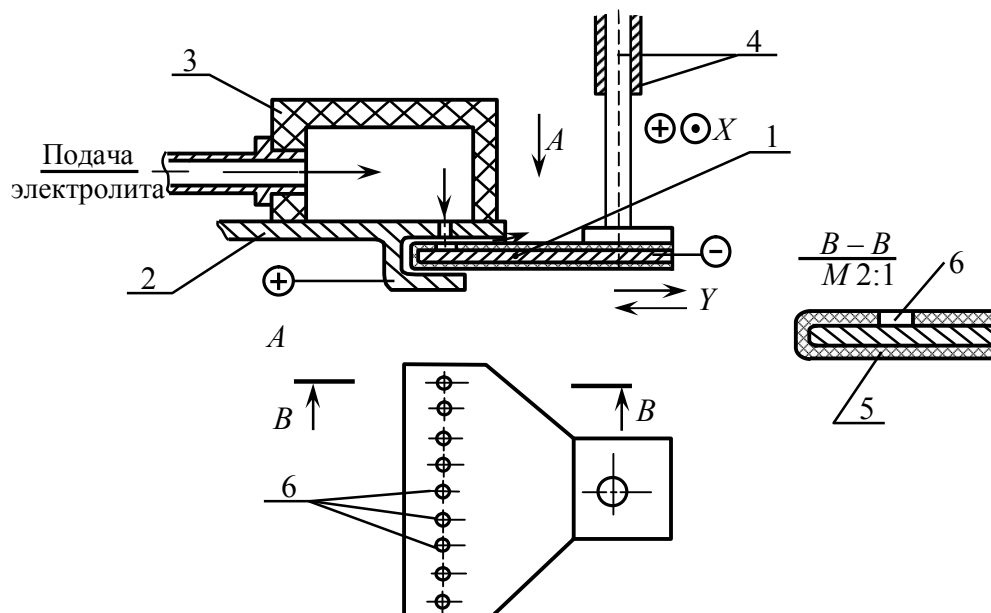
Принципиальная схема скругления острых кромок закрытых отверстий, обработанных методом электрохимической обработки: 1 – электрод-инструмент; 2 – обрабатываемая заготовка; 3 – камера приспособления; 4 – шпиндель станка; 5 – изоляционное покрытие; 6 – места съема изоляционного покрытия
